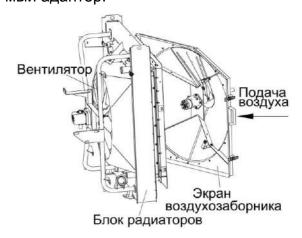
Обдувка сжатым воздухом блока радиаторов
